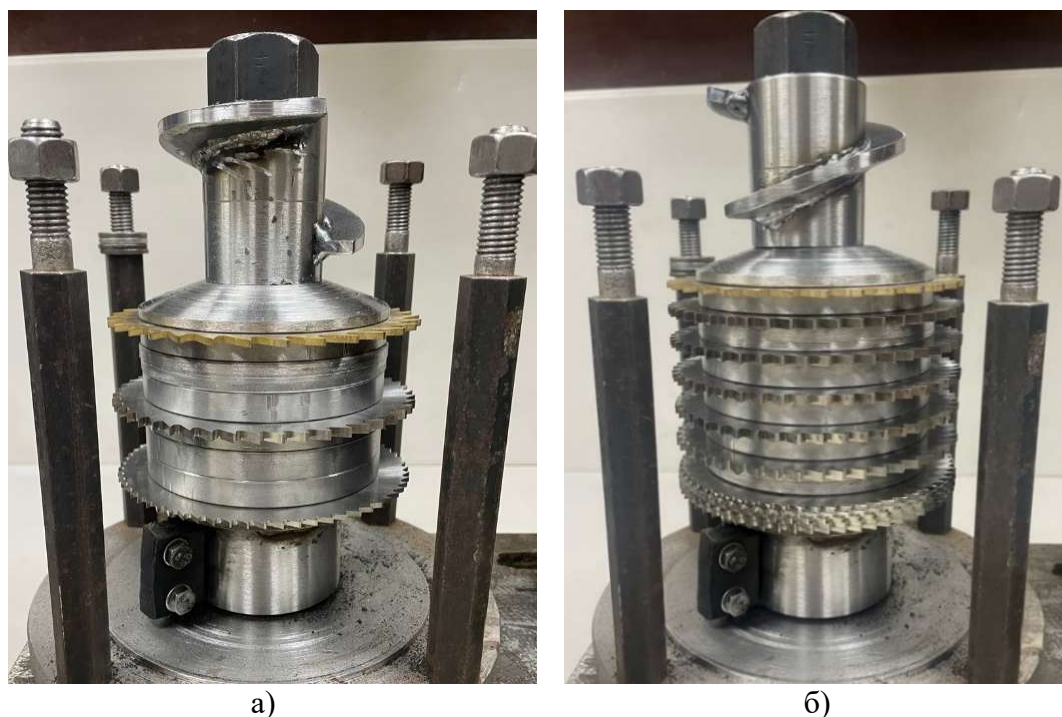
Ротор измельчителя вертикального типа в сборе:
